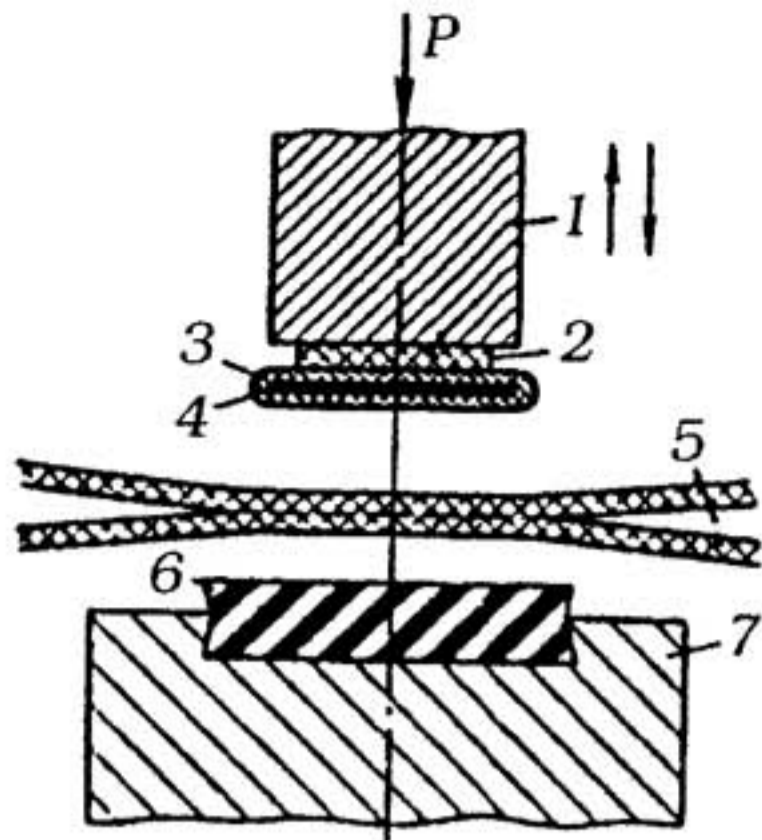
Схема термоимпульсной сварки:
